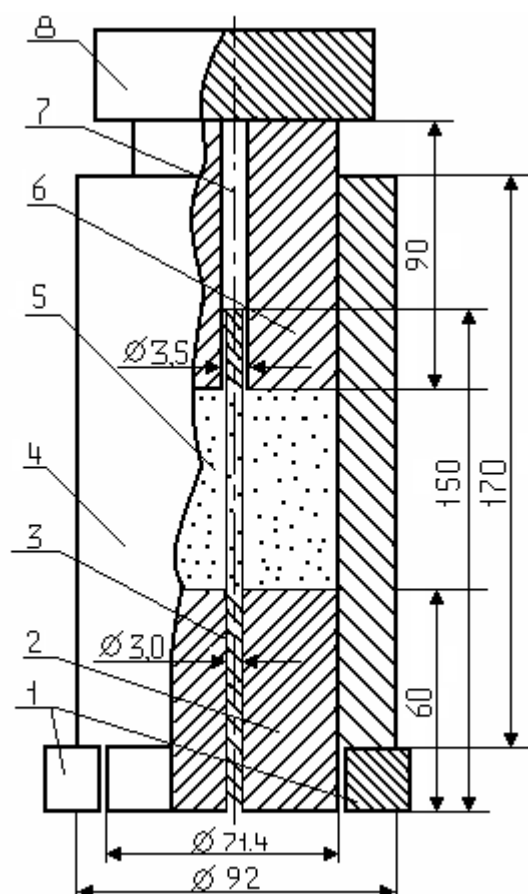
Приспособление для уплотнения образцов из холодных смесей для определения слеживаемости: 1 – подставки; 2 – нижний вкладыш формы; 3 – стальной стержень; 4 – цилиндрическая форма; 5 – образец; 6 – верхний вкладыш формы; 7 – сквозное отверстие; 8 – груз
